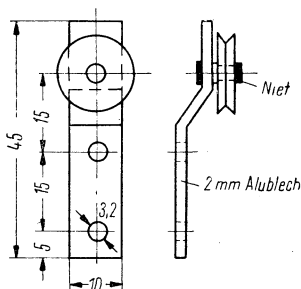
Maßskizze für die Halterung der Umlenkrolle
